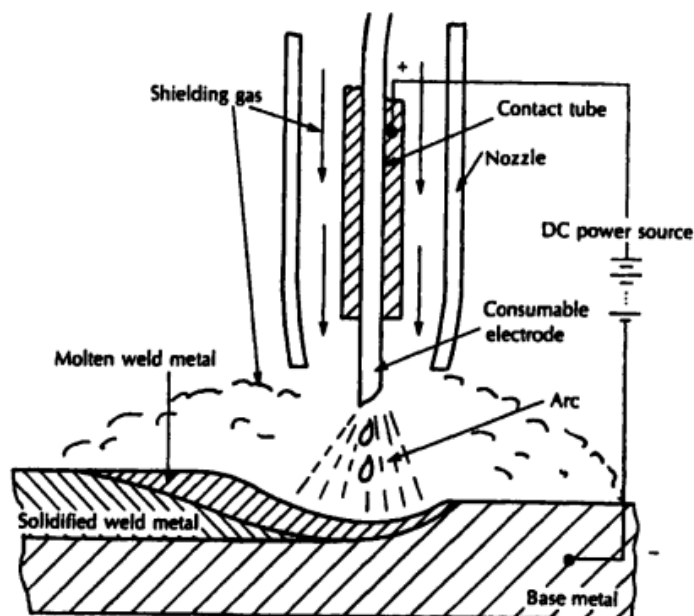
Esquema del proceso de soldadura por arco de gas y metal (GMAW), que muestra la antorcha, soldadura y conexión eléctrica
